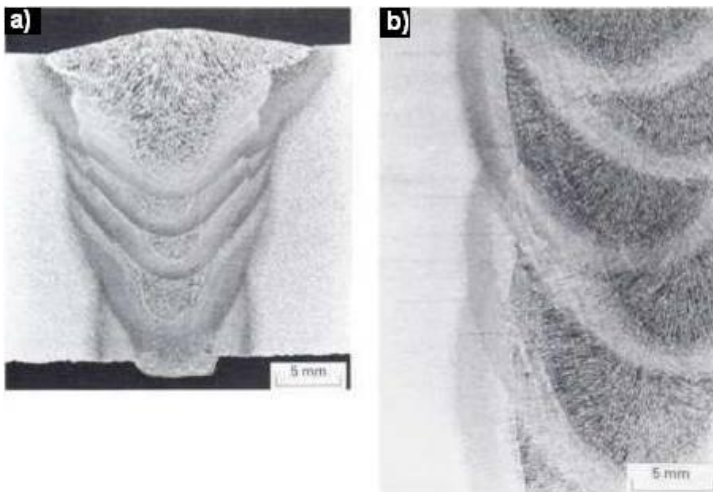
(a) macrografia de uma solda multipasses; (b) detalhe da interface MS-ZAC, onde pode ser observado o refino de grão produzido por cada passe de soldagem [26].
